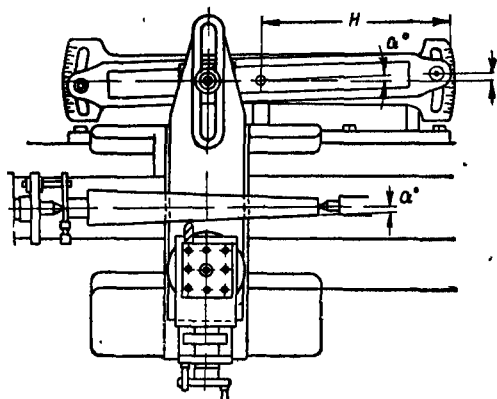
Схема обтачивания конической поверхности при помощи универсальной конусной линейки.
